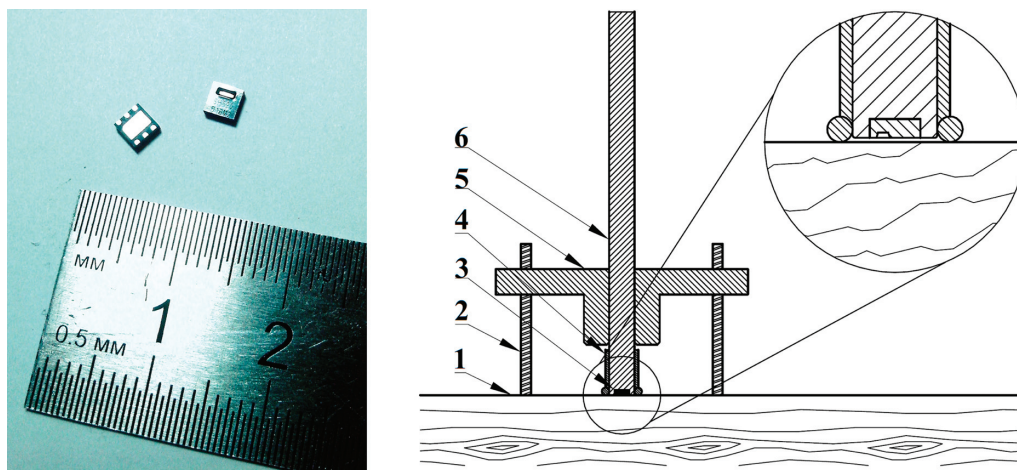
Внешний вид датчика Sensirion SHT20 (слева) и его расположение в приспособлении для измерения поверхностной влажности (справа): 1.Образец. 2.Регулировочный винт. 3. Датчик SHT20. 4.Резиновый кожух. 5.Пластиковый корпус. 6. Держатель
